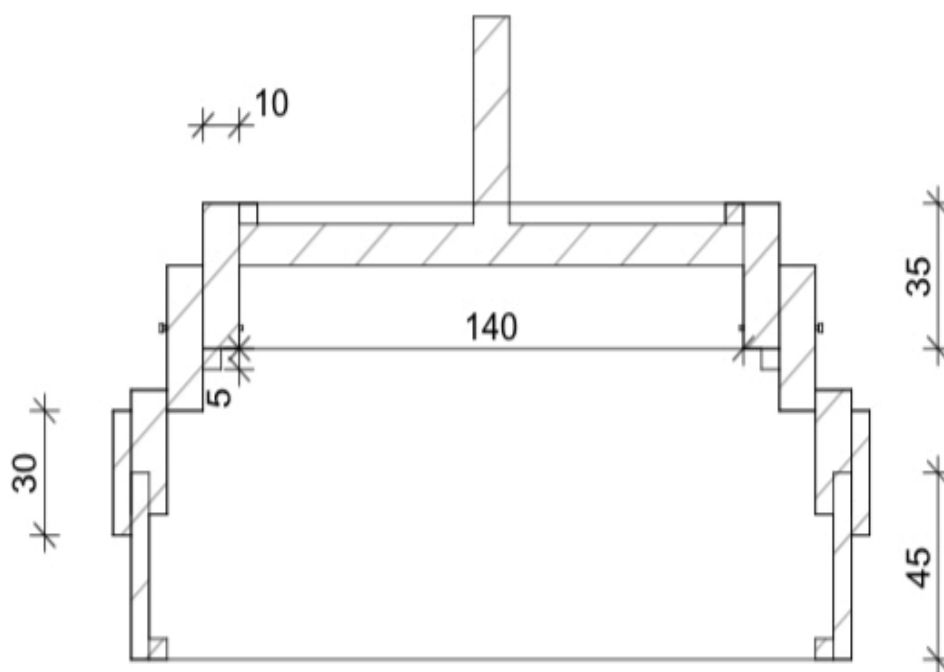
Схема насадки к разрывной машине РМ-50 для определения усилия сцепления торкрет-массы с поверхности бетонного основания
